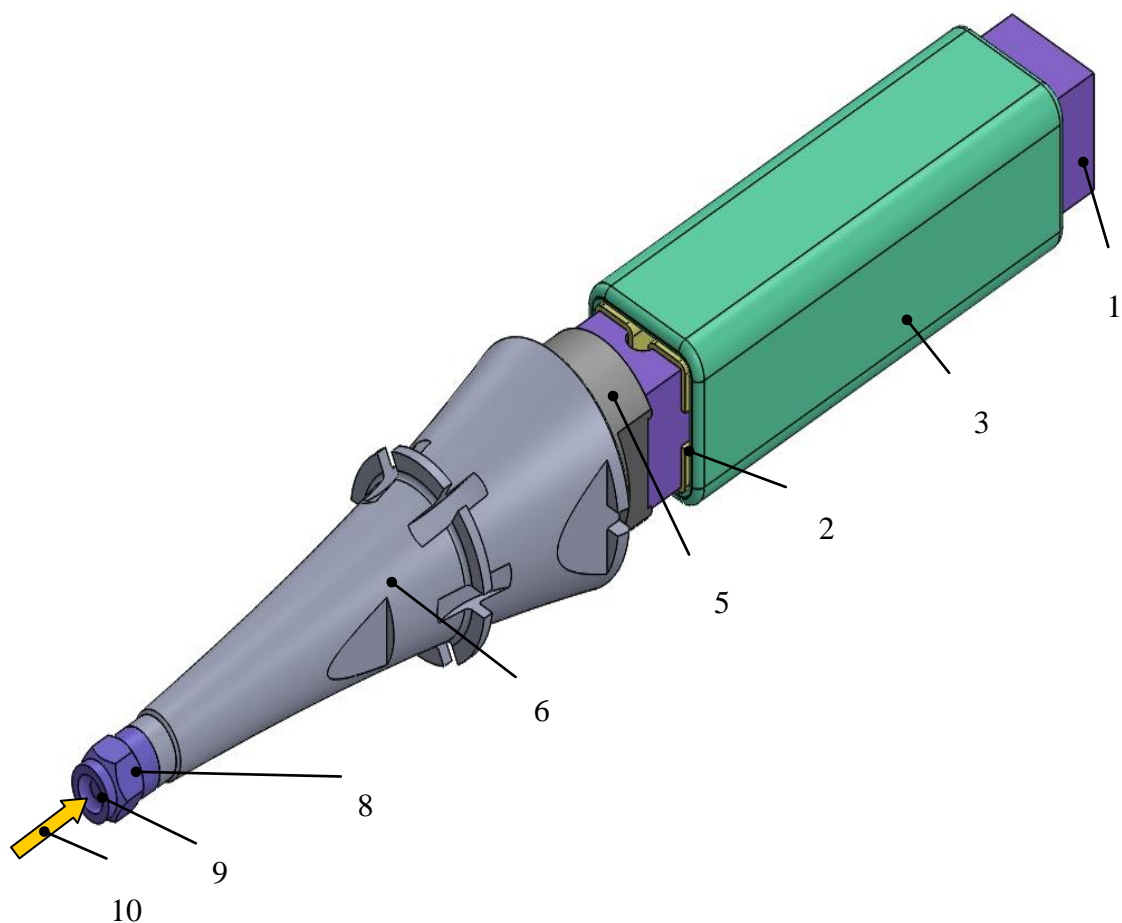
Общий вид УЗКС для ультразвуковой сварки со сменными насадками: 1 – активный элемент (двигатель); 2 – щеки защитные; 3 – обмотка подмагничивания-возбуждения; 5 – переходник; 6 – бустер; 8 – насадка сменная; 9 – рабочий торец насадки; 10 – нагрузка со стороны зоны сварки
